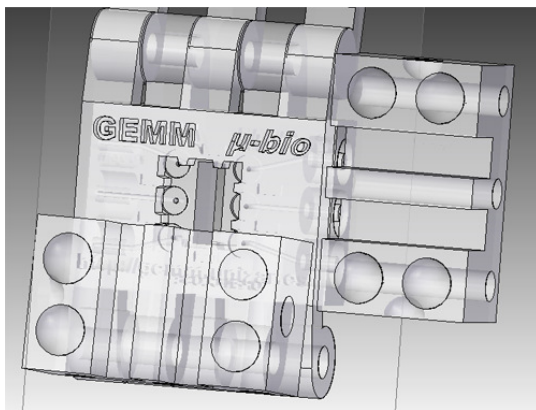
Representación 3D CAD del conjunto encapsulado-piezas patrón.
